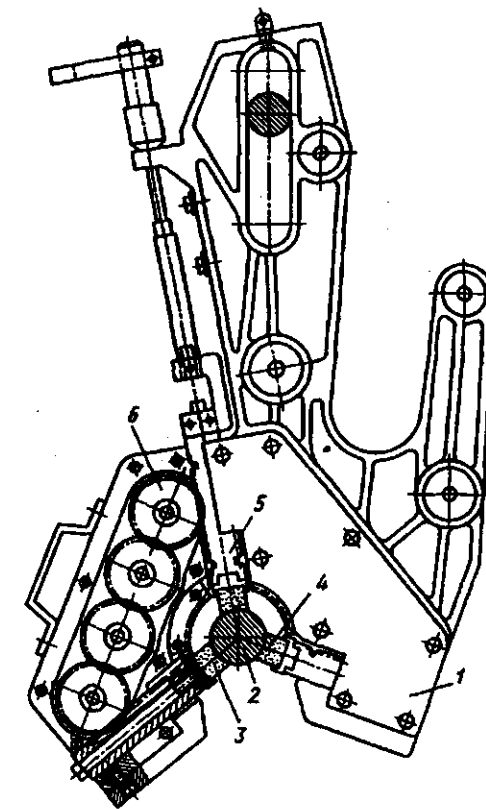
Схема суперфинишной обработки с охватывающим расположением брусков
